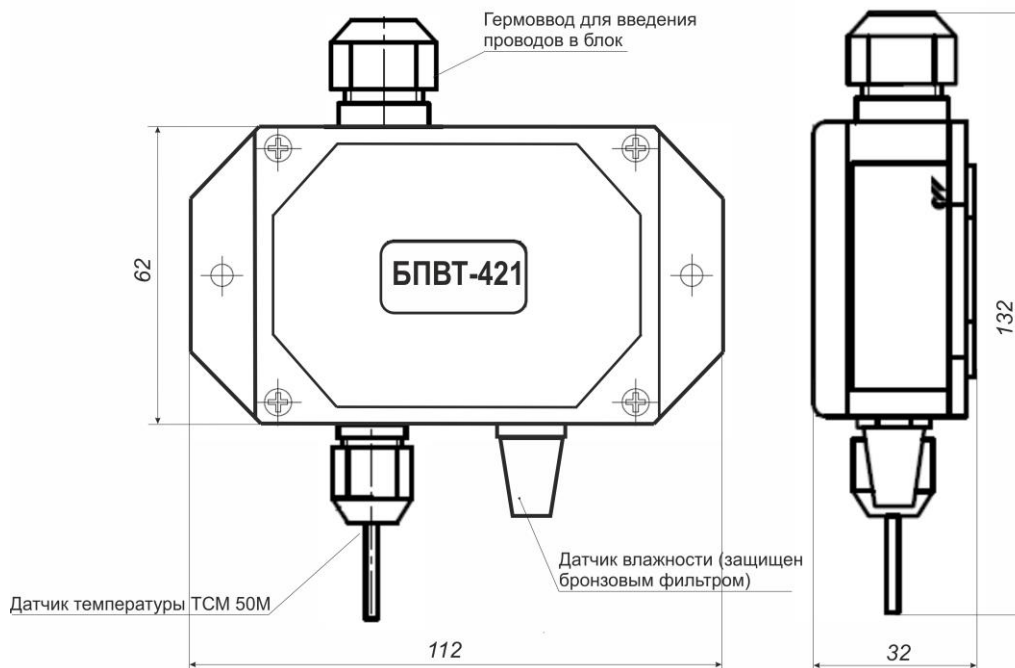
Внешний вид и габаритные размеры блока БПВТ-421
